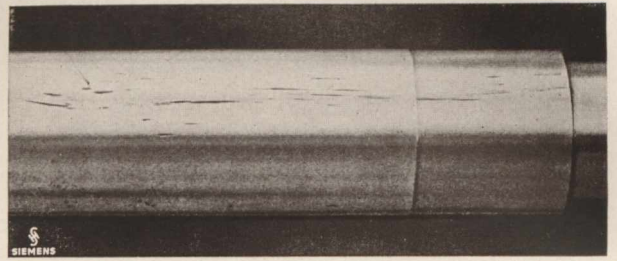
Magnetpulverbild einer im Betrieb schadhaft gewordenen Fräsmaschine
